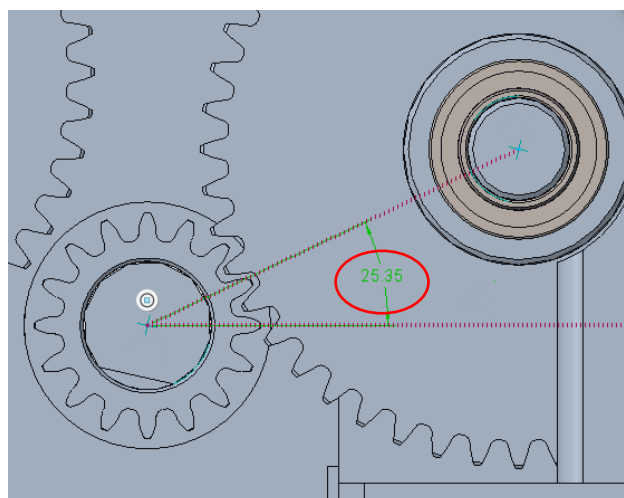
Ángulo entre el plano que contiene los ejes y el plano horizontal
